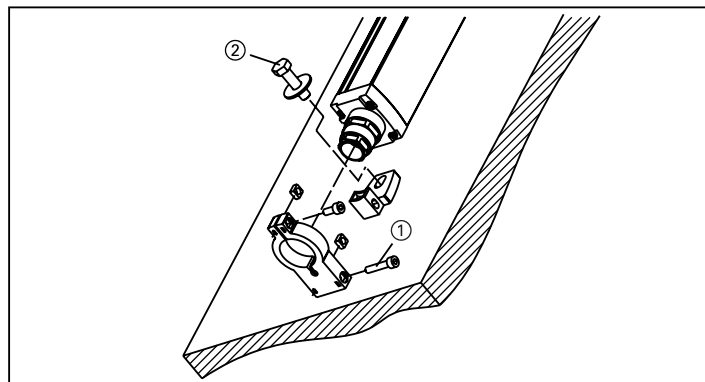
Montagem do C 2000, M 2000, e M 2000-A/P com suportes-swivel-mount
